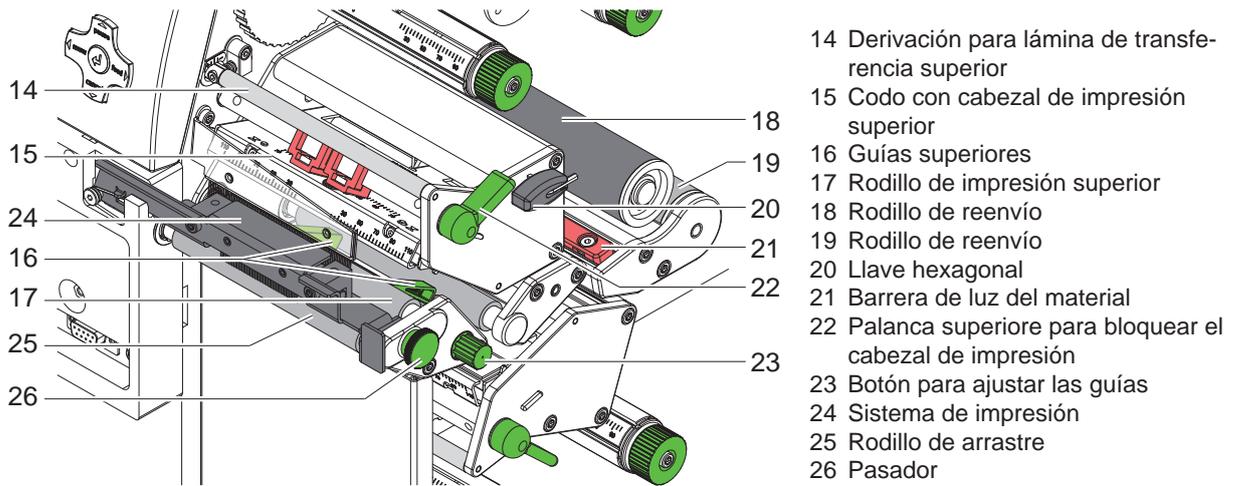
Mecanismo de impresión - módulo superior de impresión XD4T
